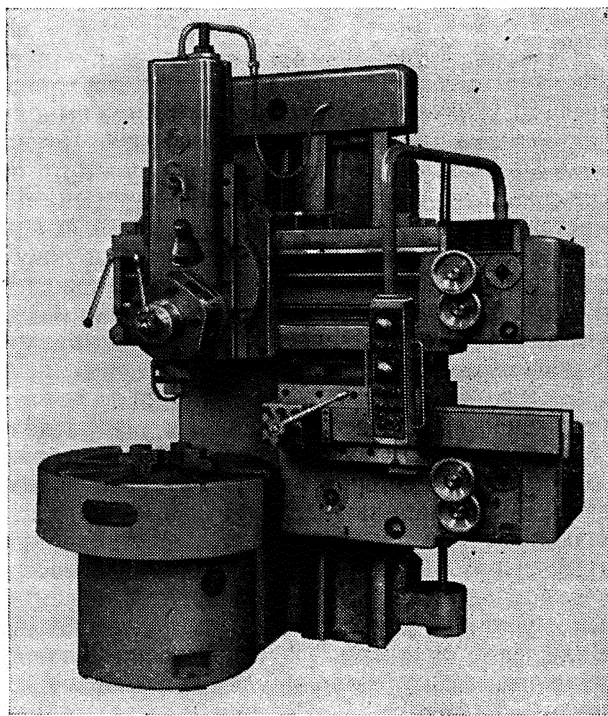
Токарно-карусельный одностоечный универсальный станок мод. 1510
